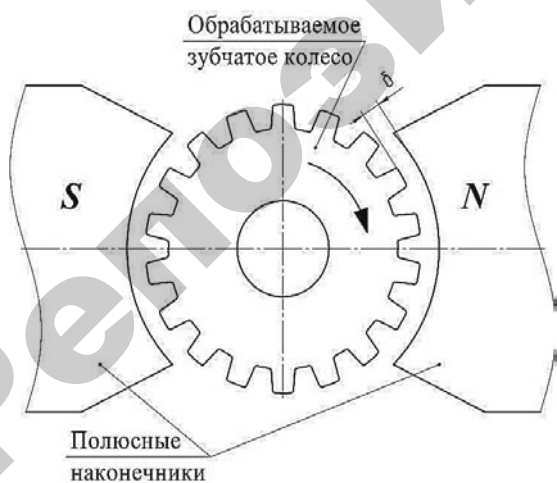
Схема магнитно-абразивной обработки мелкозубчатых цилиндрических зубчатых колес
